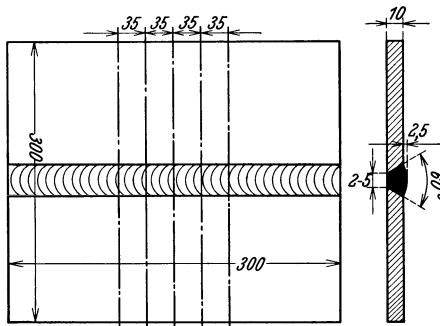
Stumpfgeschweißte Blechplatten, über deren Schweißnaht die Probestreifen für Zug- und Biegeproben gelegt werden.
